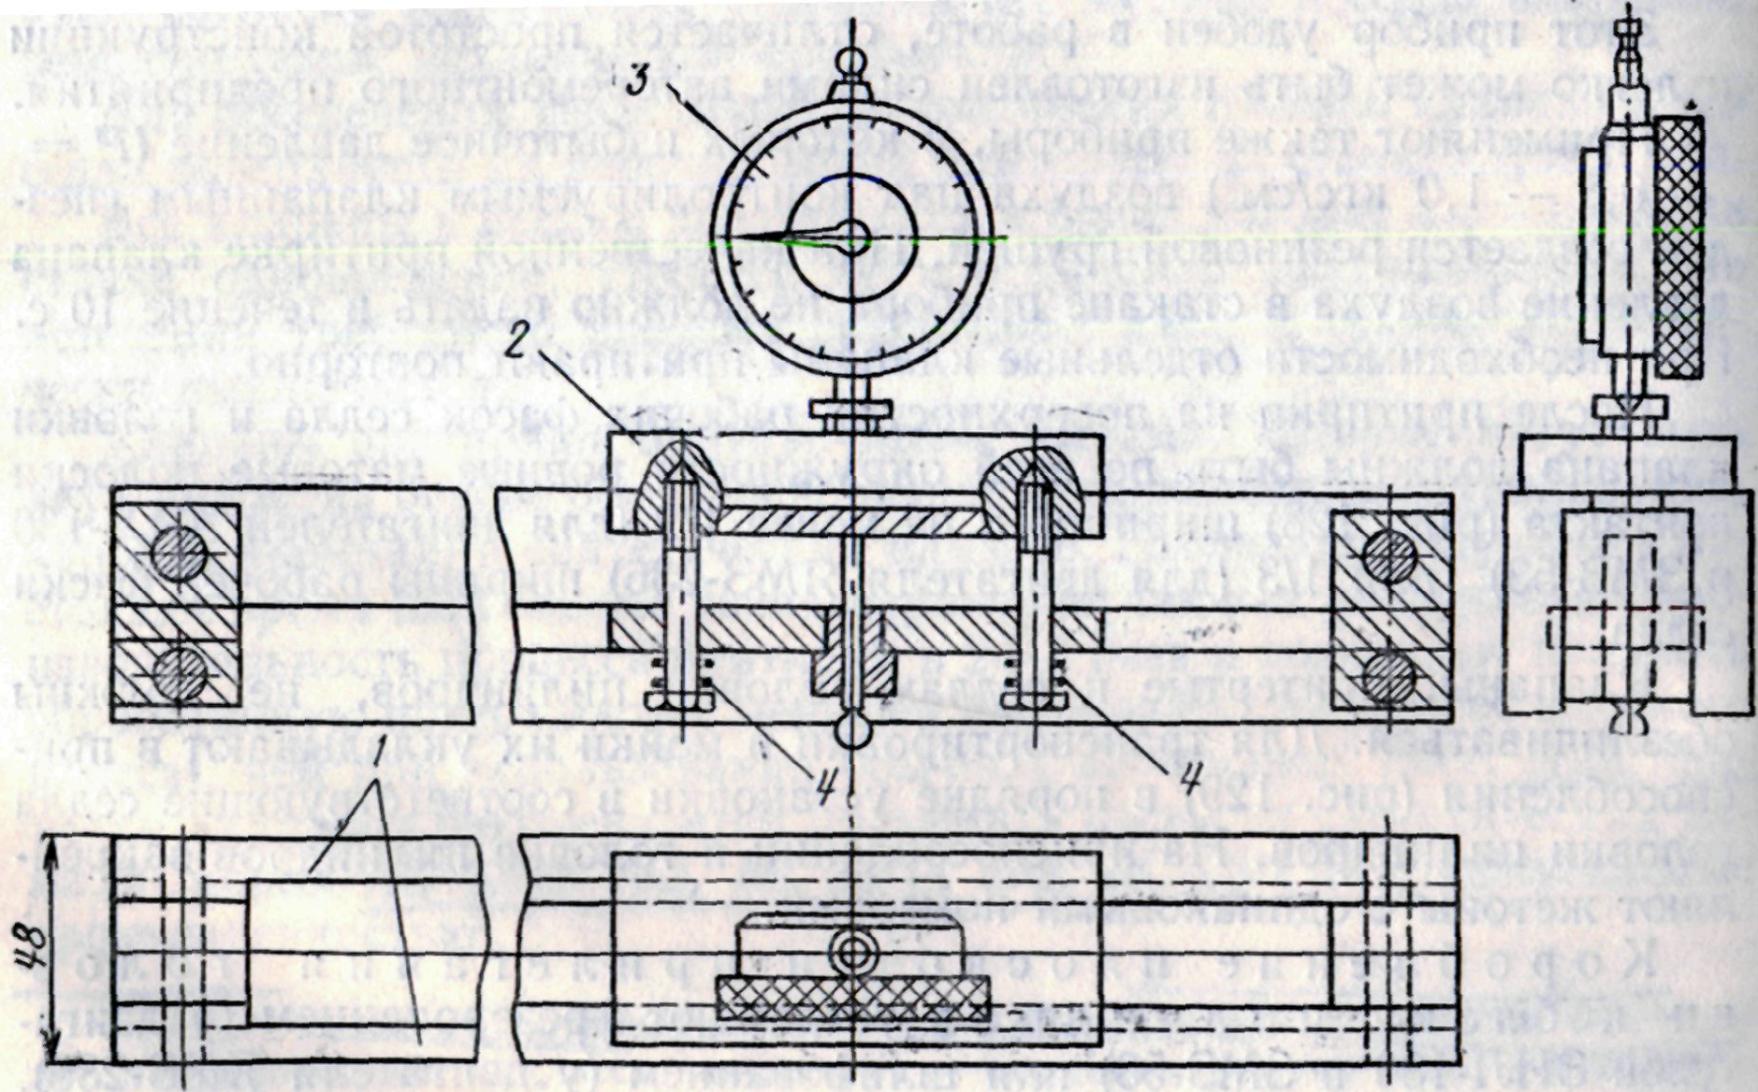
Приспособление для контроля плоскостности привалочных поверхностей головки и блока цилиндров двигателя
